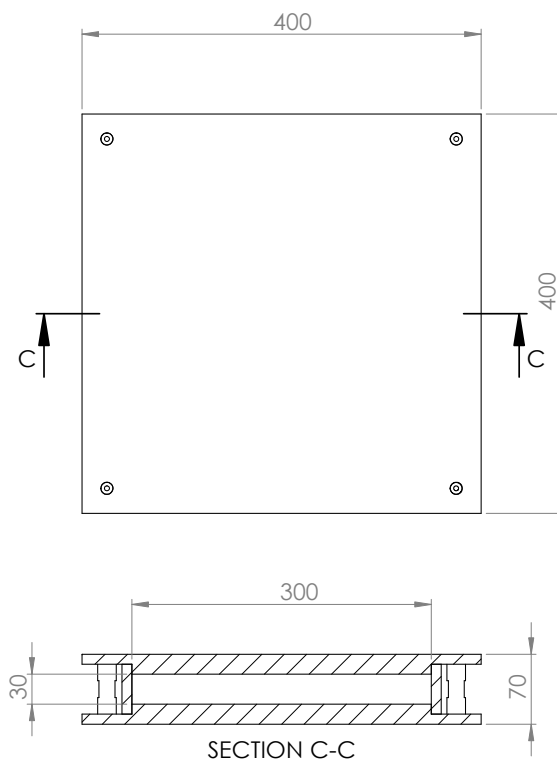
Molde de Alumínio fechado e respetivas dimensões gerais, em mm.
